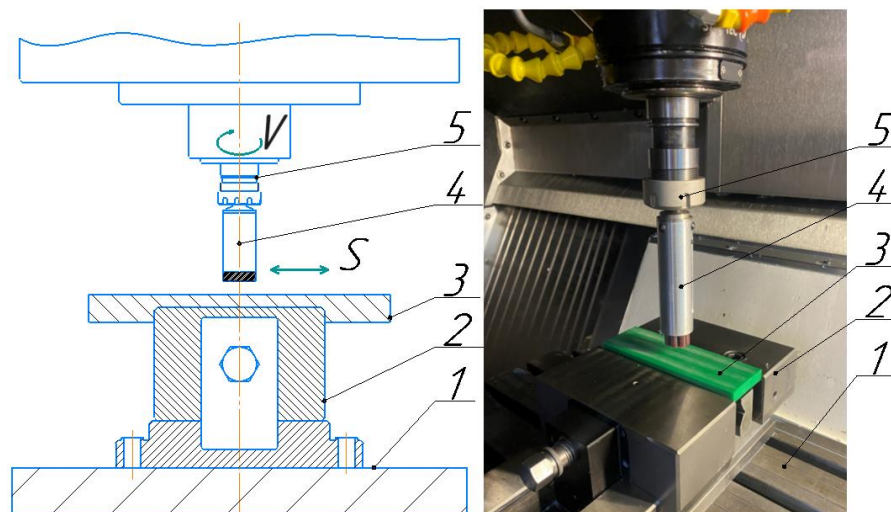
схема обработки. 1 — Станина, 2 — приспособление для закрепления детали (тиски), 3 — обрабатываемая деталь, 4 — щётка с гибким керамическим ворсом, 5 — шпиндель.
